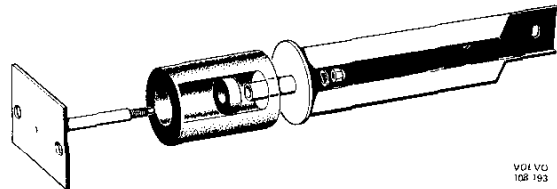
Stoßfängerbefestigung (übrige Märkte außer USA)
